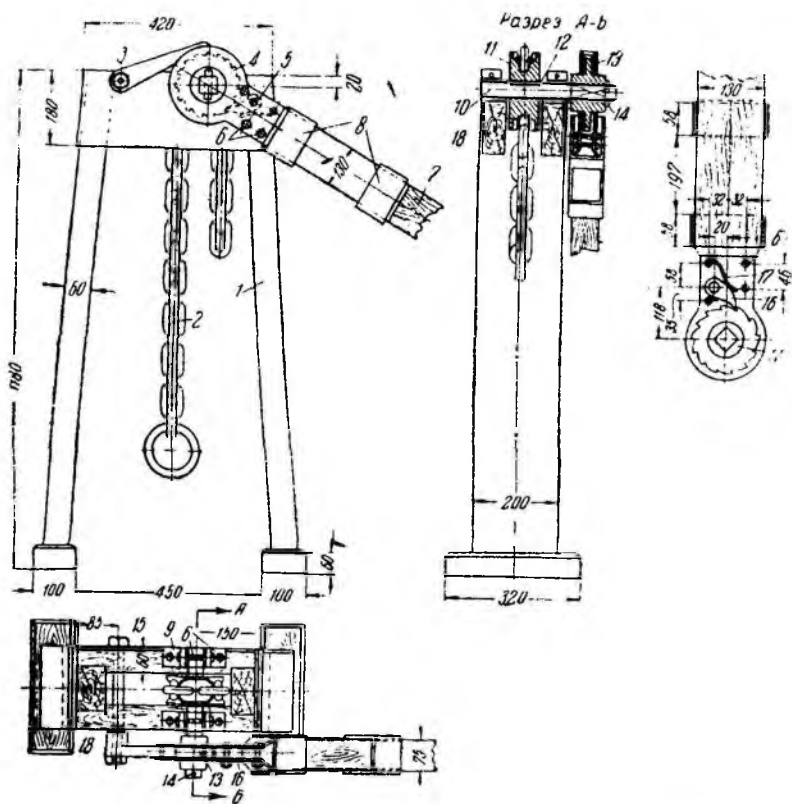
Корчевальный станок «Стахановец»: 1 — станина; 2 — цепь; 3 — собачка верхняя; 4 — щёчка трещотки; 5 — ось собачки; 6 — болты с гайкой $d = 1\frac{1}{2}$ "; 7 — ручка рычага; 8 — хомуты ручки; 9 — подшипники; 10 — вал (чугунный); 11 — звёздочки для цепи (наружные); 12 — шпонка; 13 — храповик; 14 — шпилька; 15 — болт для собачки $d = 1$ "; 16 — собачка нижняя; 17 — пружина для нижней собачки; 18 — стяжное кольцо станины
